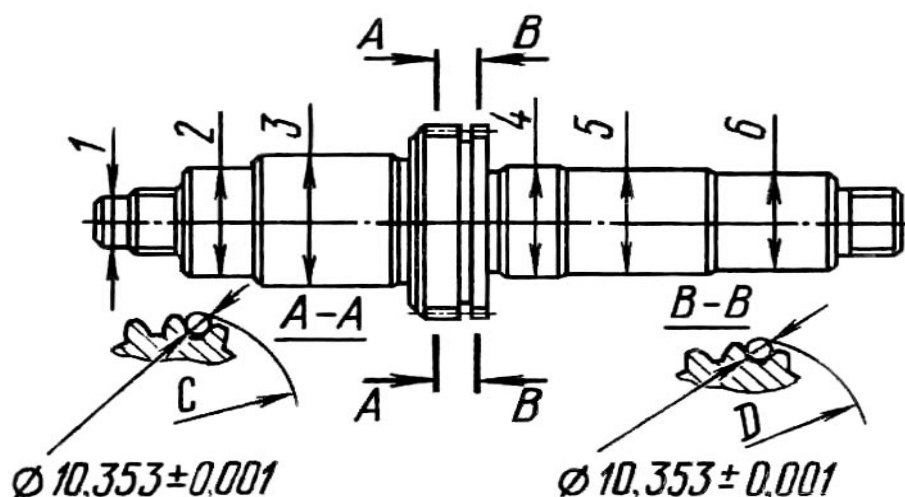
Расположение шеек промежуточного вала раздаточной коробки:
